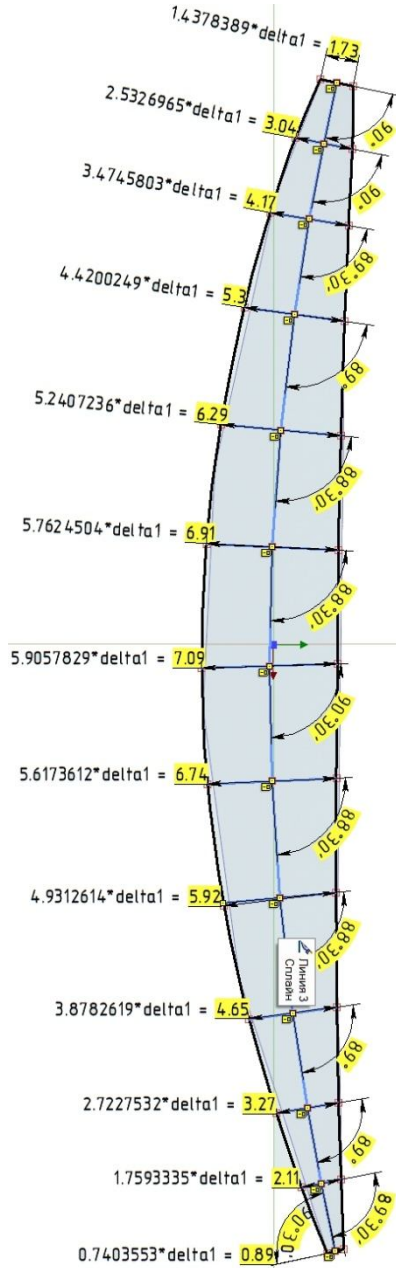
3D-профиль лопатки с центральными точками
